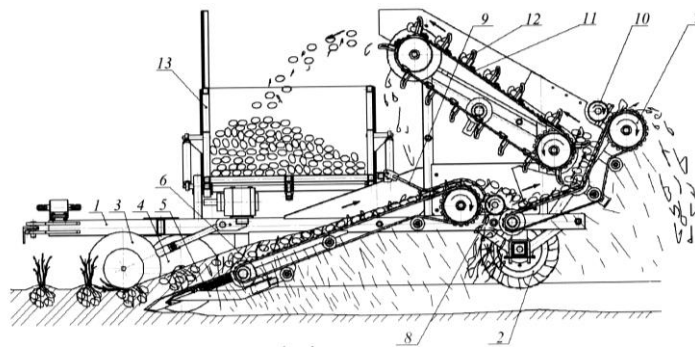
Конструктивно-функціональна схема картоплезбирального комбайна КПБ-1: 1 – рама; 2 – ходові колеса; 3 – опорний коток; 4 – відрізні диски; 5 – лемеші; 6 – приймальний транспортер; 7 – передавальний Г-подібний транспортер; 8 – приймальний валець; 9 – бадиллєвловлювальні прутки; 10 – відбійний валець; 11 – завантажувальний транспортер; 12 – скребки завантажувального транспортера; 13 – бункер
